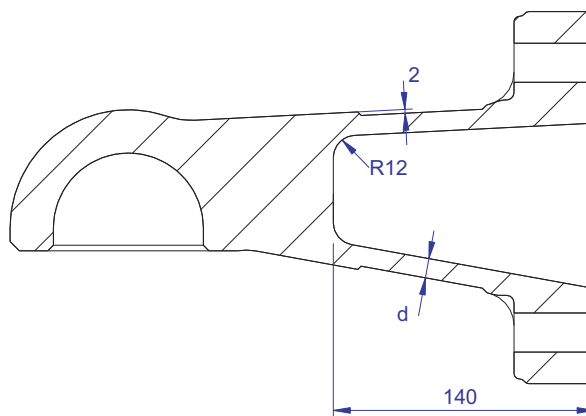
Dimensions del forat mecanitzat a la part posterior de l'enganxall
